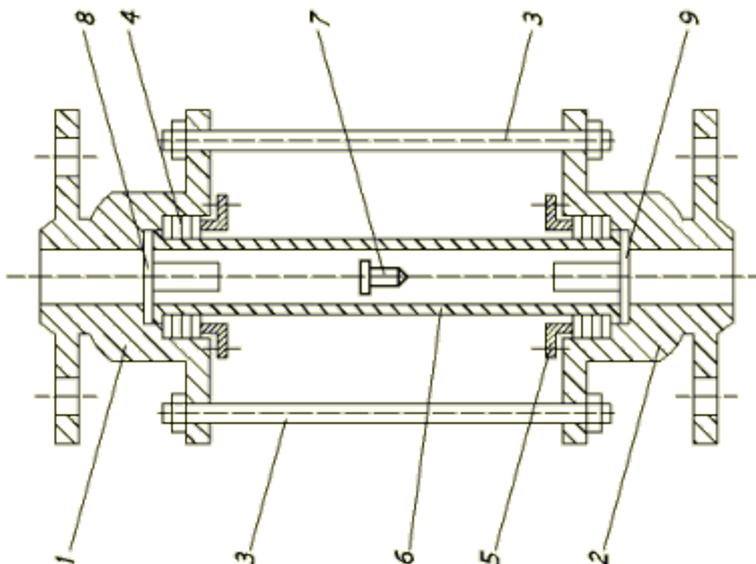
Устройство ротаметра: 1 – верхний патрубок; 2 – нижний патрубок; 3 – болтовые стержни; 4 – накидные гайки; 5 – сальник уплотнитель; 6 – стеклянная трубка; 7 – поплавок; 8 – верхний упор; 9 – нижний упор
